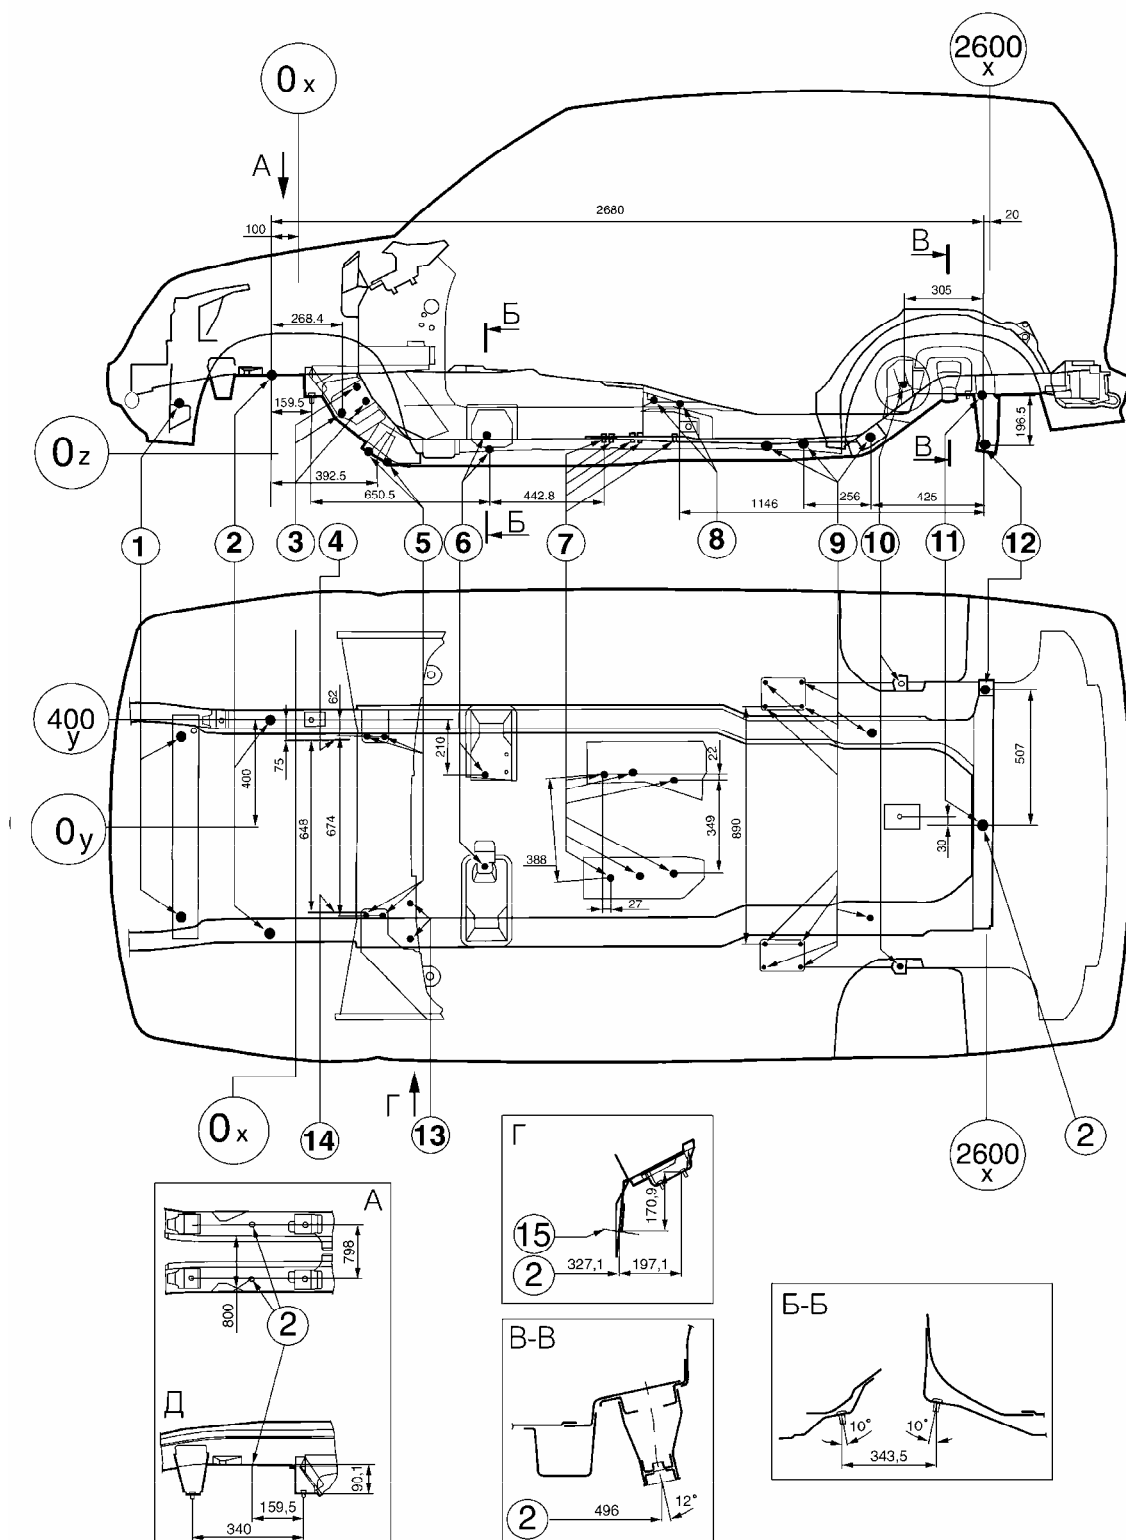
Основные справочные размеры точек крепления узлов и агрегатов автомобиля:
